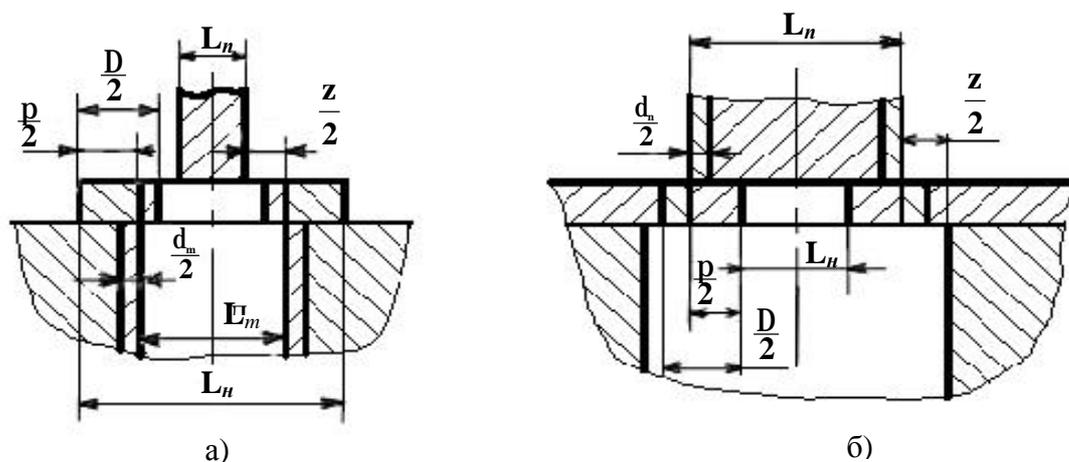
Схема условного расположения допусков и зазоров: а – размеры, увеличивающиеся при износе штампа; б – размеры, уменьшающиеся при износе штампа.
